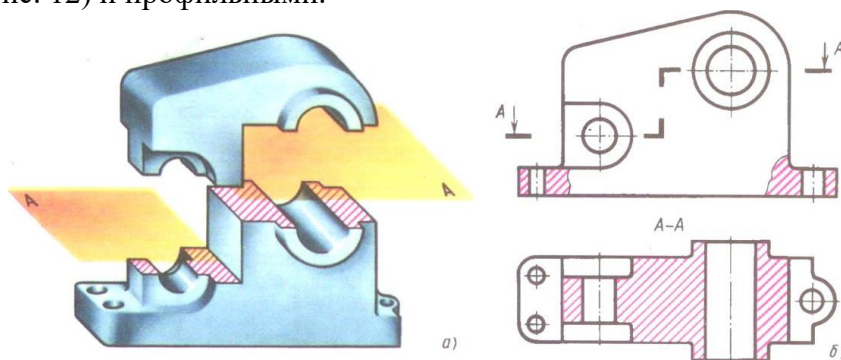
Сложный ступенчатый горизонтальный разрез
